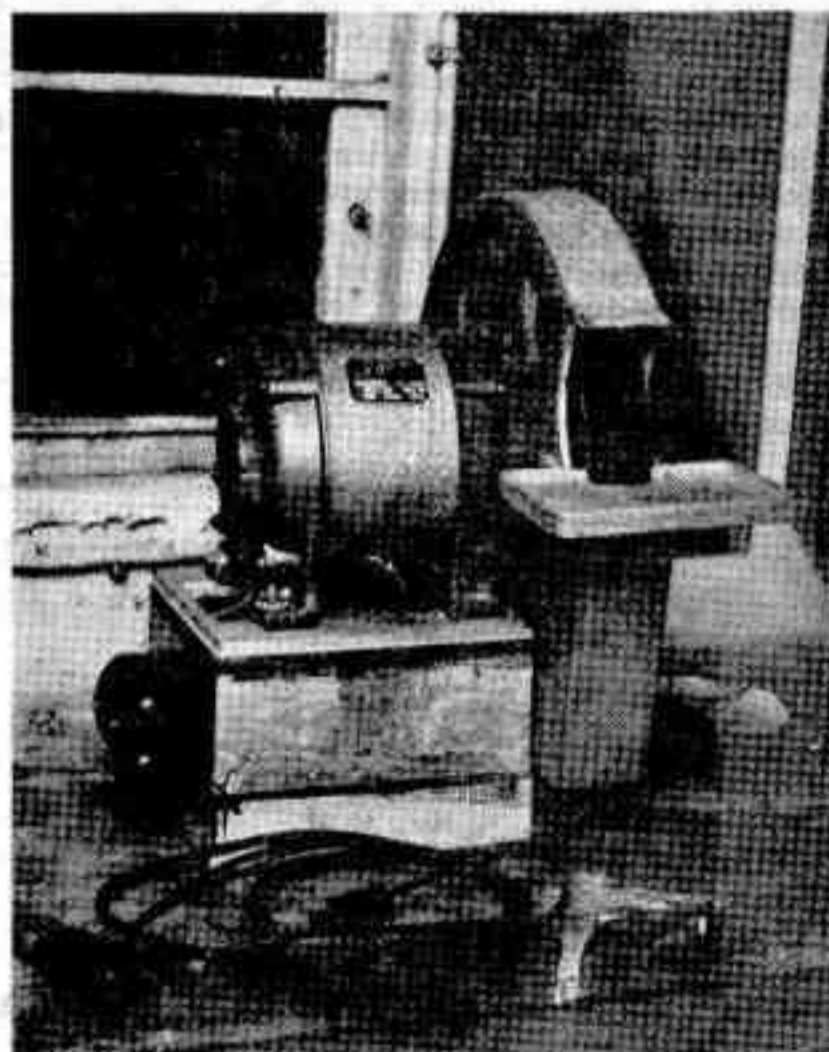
MÁQUINA BISELADORA FRONTAL A CINTA.
